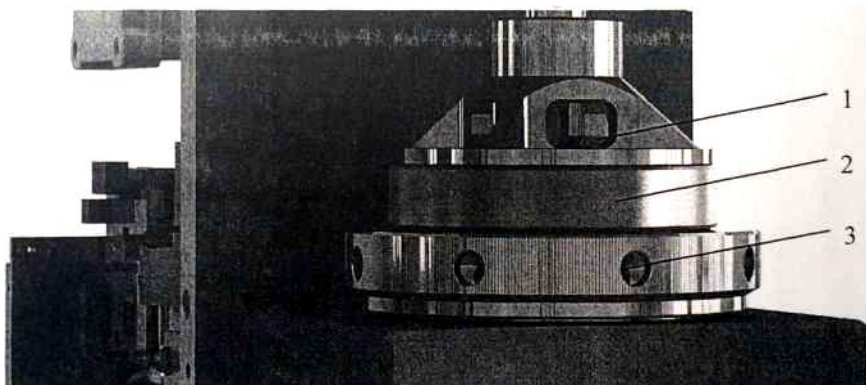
Установка пластины в рабочий зазор приладу:
